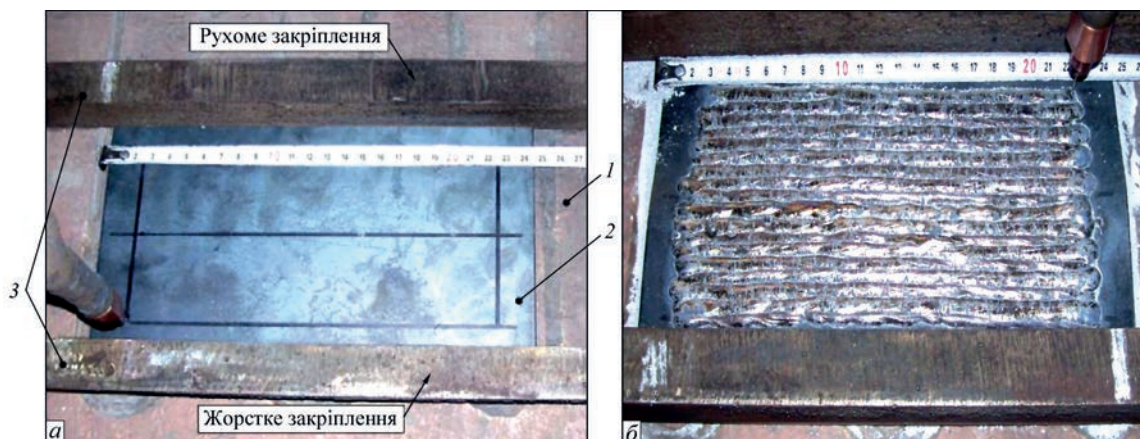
Спосіб закріплення пластин на зварювальному столі (*а*): 1 – зварювальний стіл з мідною пластиною, 2 – пластина, що наплавляється, 3 – притисні планки; (*б*) – зовнішній вигляд пластини після напавлення
